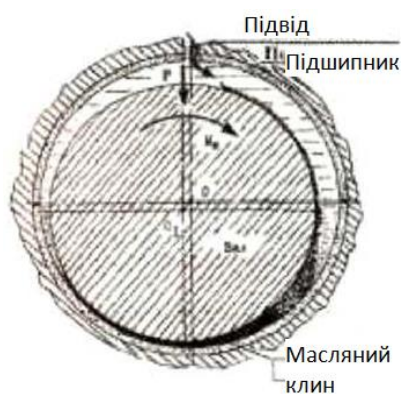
Поперечний переріз шийки колінчатого вала
